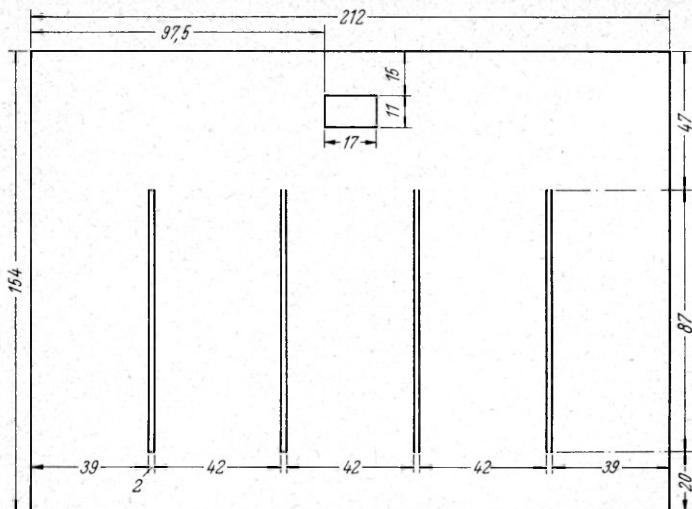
Maßskizze der Frontplatte mit Ausschnitten
